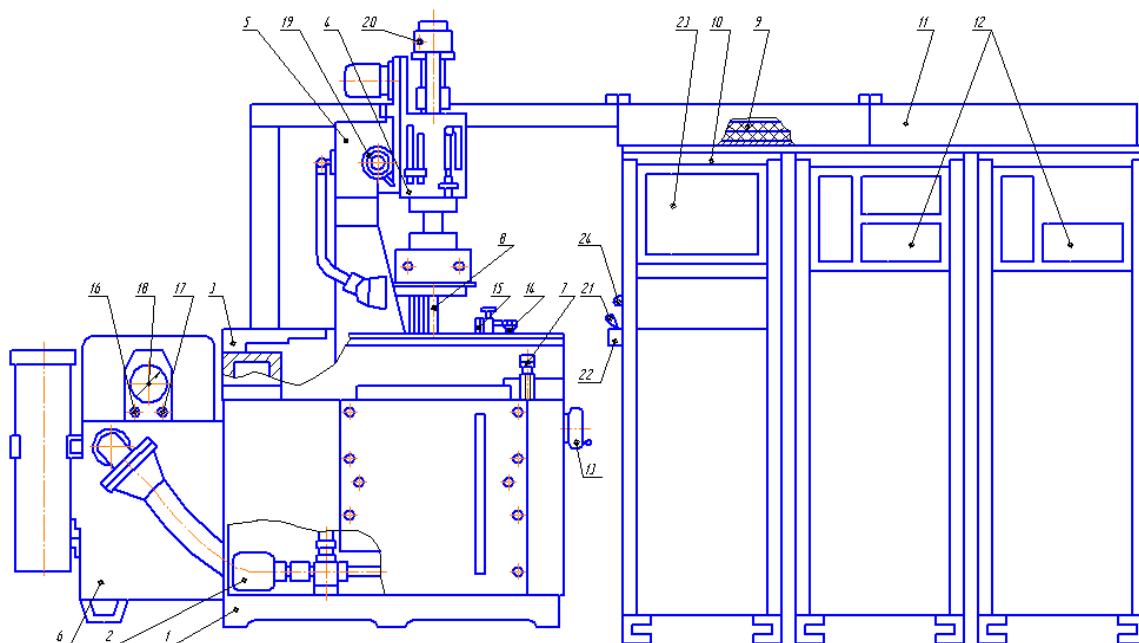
Общий вид станка модели 4E723-01.Ф.
